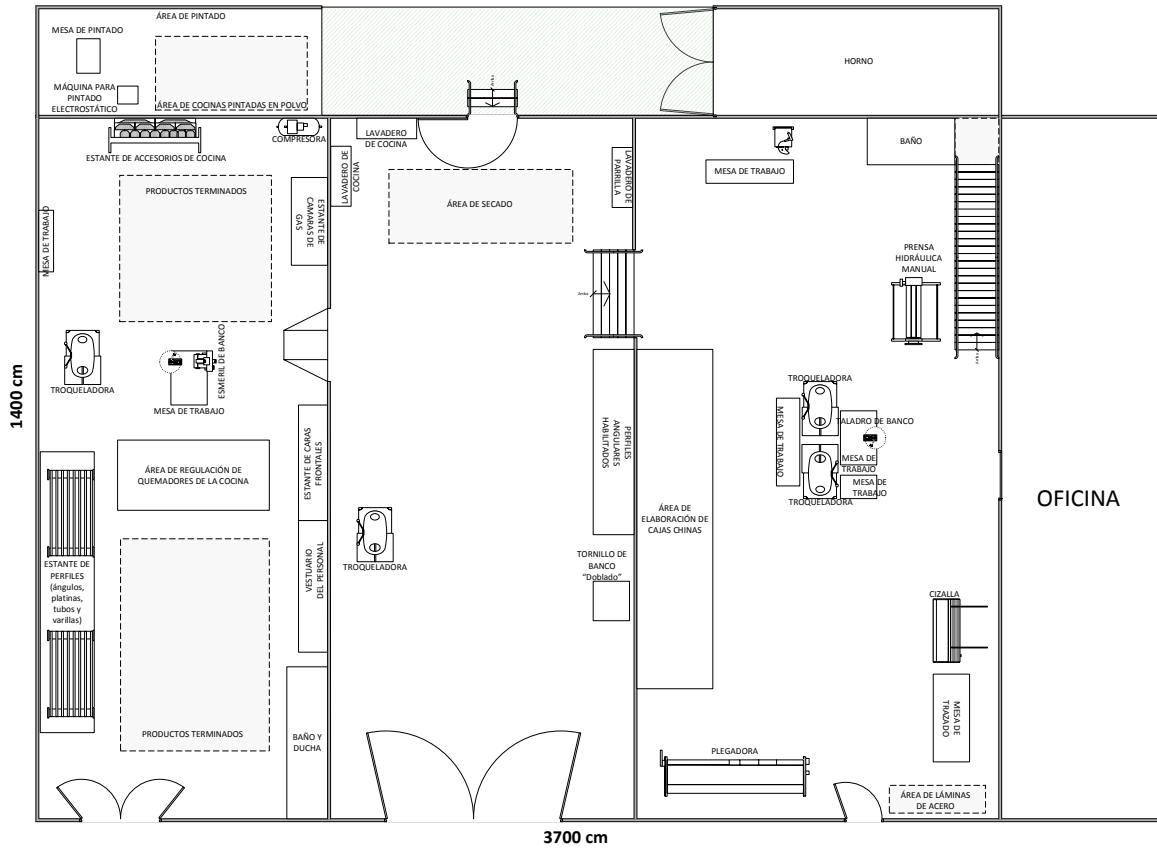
Distribución de la planta nivel 1 de la empresa Solisgas SAC.
